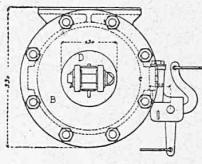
Horizontalschnitt und Grundriss.
